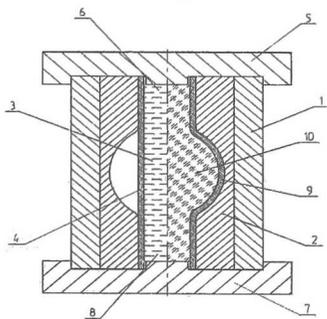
Штамп для раздачи трубчатой заготовки с использованием энергии расширения воды при ее заморозке
